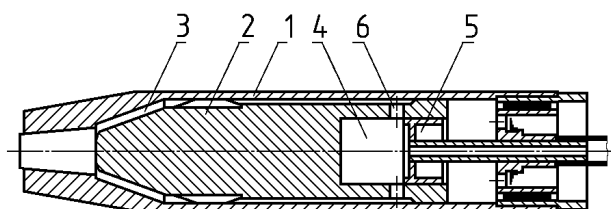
Пневмопробойник: 1 – корпус; 2 – ударная часть; 3 – камера холостого хода; 4 – камера рабочего хода; 5 – воздухораспределительный патрубок; 6 – поперечное впускное отверстие.
